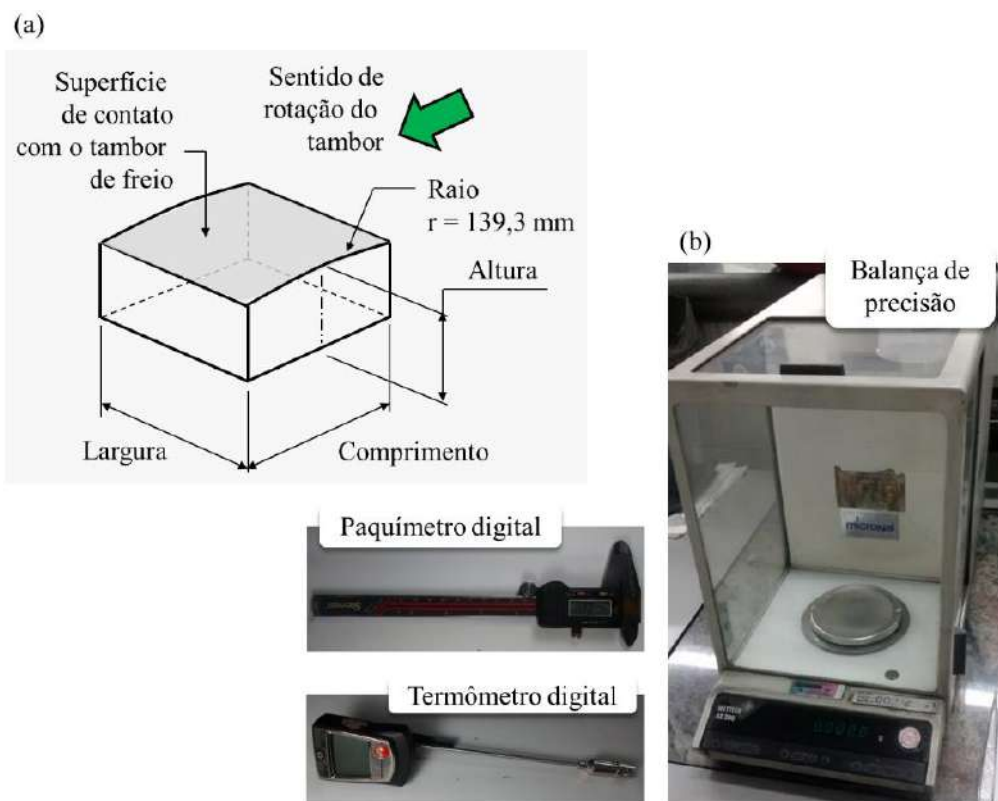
(a) Esquema Mostrando Detalhe Dimensional dos Corpos de Prova; (b) Equipamentos de Medição Utilizados Durante os Ensaio de Desgaste em Escala – Cortesia
